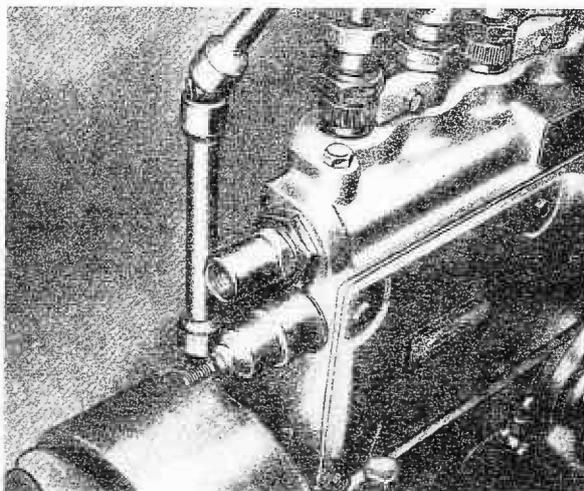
Lösen der Halteschrauben an der Einspritzpumpe mit Gelenksteckschlüssel
